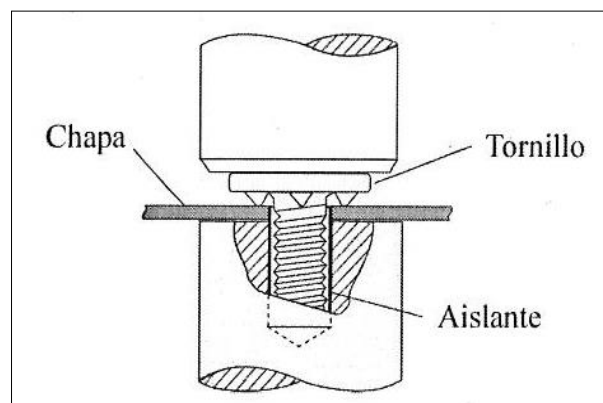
Tornillo a ser soldado por proyección, alojado en el electrodo inferior.
